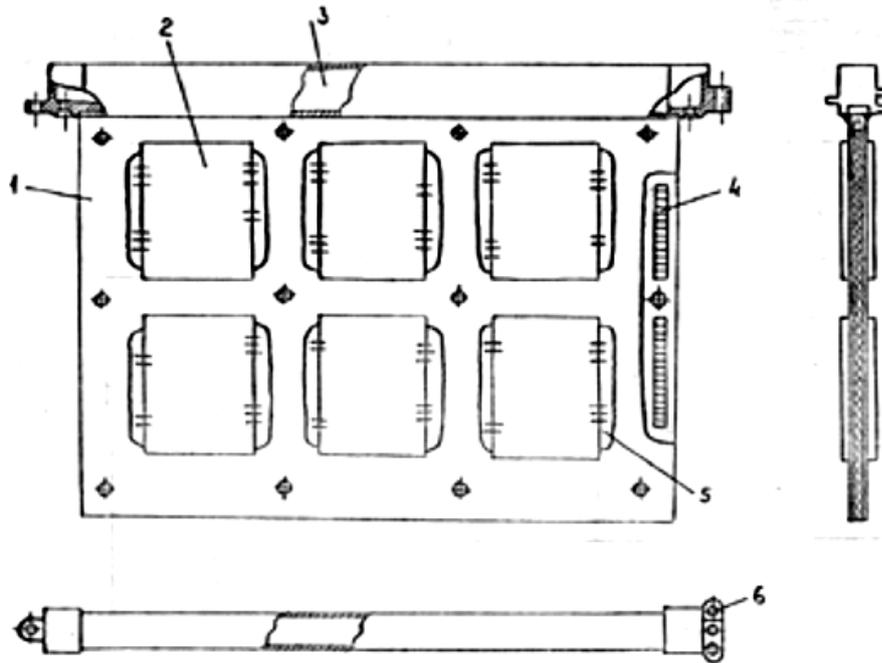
Конструкция двухсторонней ФЯ на металлическом П-образном основании: 1 - П-образная пластина (металлическая обкладка); 2 - МСБ; 3 - воздуховод; 4 - печатная контактная площадка; 5 - зона коммутации МСБ с ПП; 6 - шарнир
